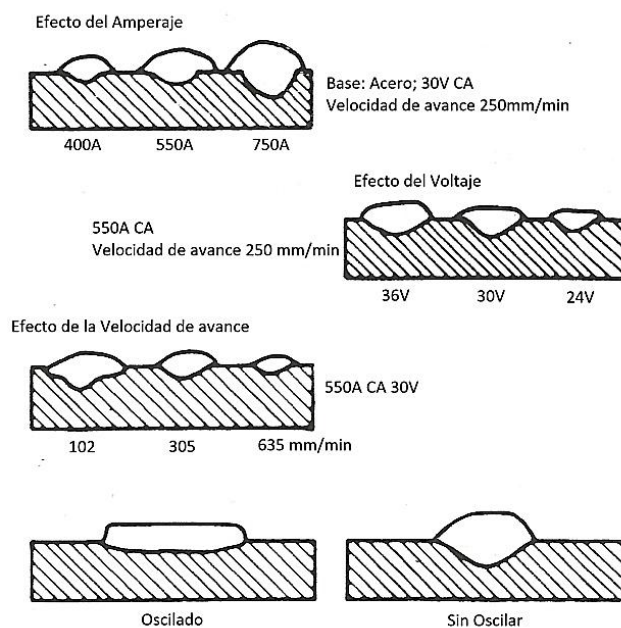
Efecto de los parámetros de soldadura en cordón y penetración. (The Welding Institute, 1980)
